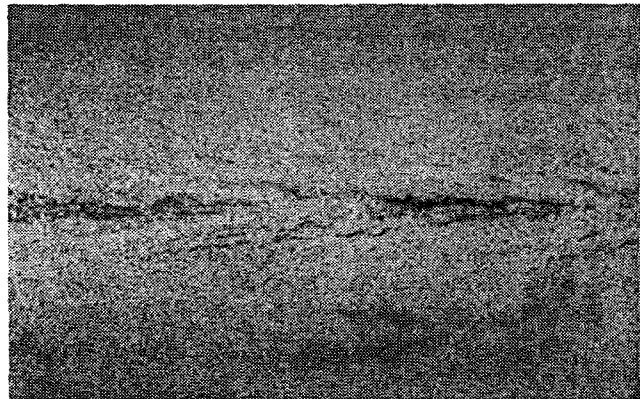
Макроструктура продольного сечения литой заготовки из стали 70К
